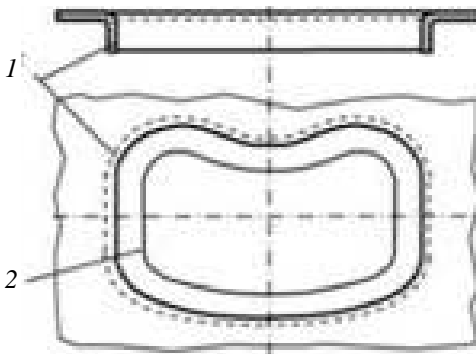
Отбортовка отверстия сложной формы: 1 – борт; 2 – исходное отверстие в плоской заготовке
